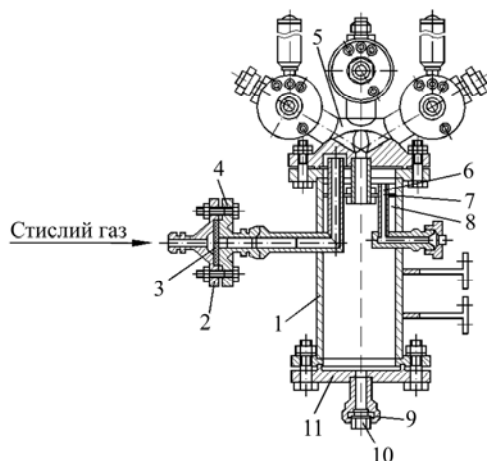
Прилад постійного тиску установки: 1 — корпус фільтра, 2 — кришка клапана, 3 — мембрана, 4 — корпус клапана, 5 — блок камер згоряння, 6 — зливний патрубок, 7 — механічний дисковий фільтр, 8 — вода, 9 — гайка, 10 — заглушка, 11 — кришка фільтра
